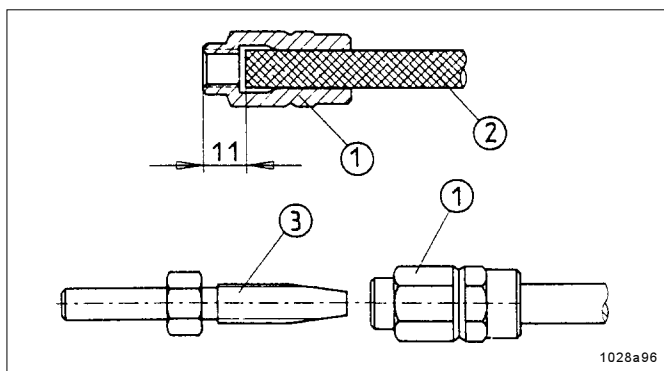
Prémontage des douilles filetées et des embouts pour tuyau sur la conduite principale
